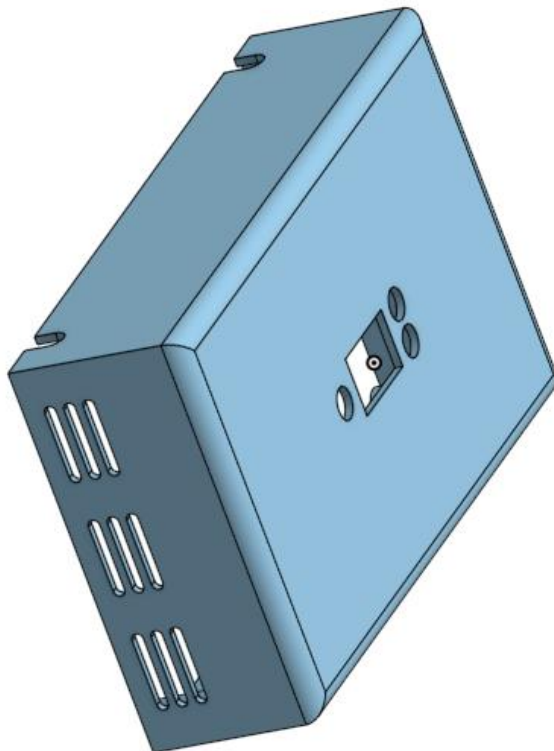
3D-модель основної частини корпусу внутрішнього блоку
